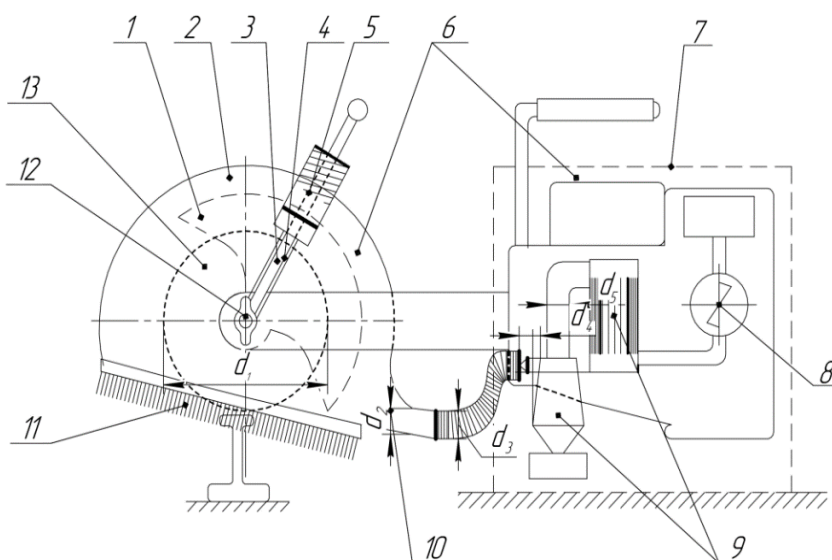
Расчетная схема: 1 - внутренний пылеотсасывающий элемент; 2 - внешний силиконовый подвижный пылеотсасывающий кожух; 3 - прорези; 4 - вилочная рукоятка-шток; 5 - пружинный механизм; 6 - система защиты от шума; 7 - звукопоглощающий кожух; 8 - фильтро-вентиляционный моноблок; 9 - двухступенчатая пылеочистка; 10 - патрубок отвода пыли и гибкая трубка; 11 - щетинистое ограждение из нитей термоупругого демпфирующего титаноникелевого сплава; 12 - гайки-барашки; 13 - отрезной диск
